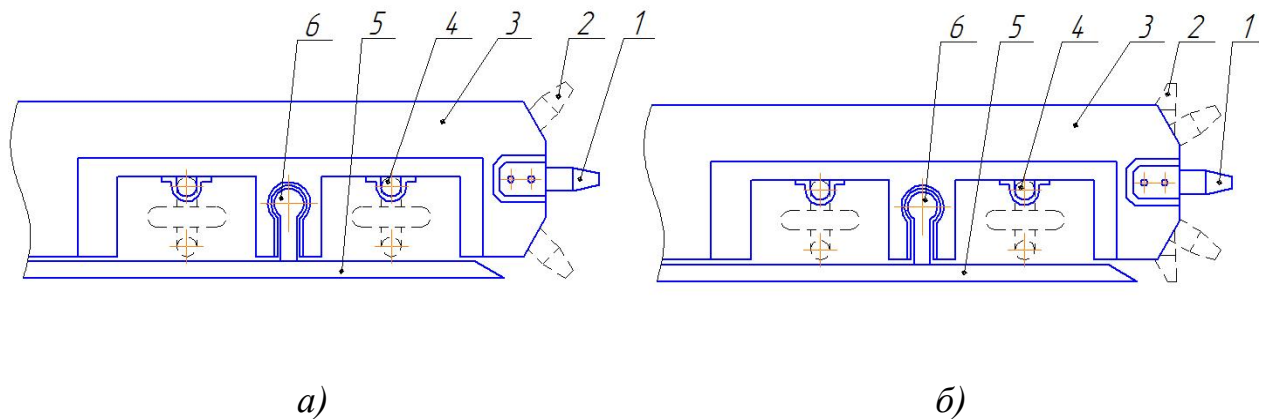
Схема расположения резцов на скребках ЗЗСК:
